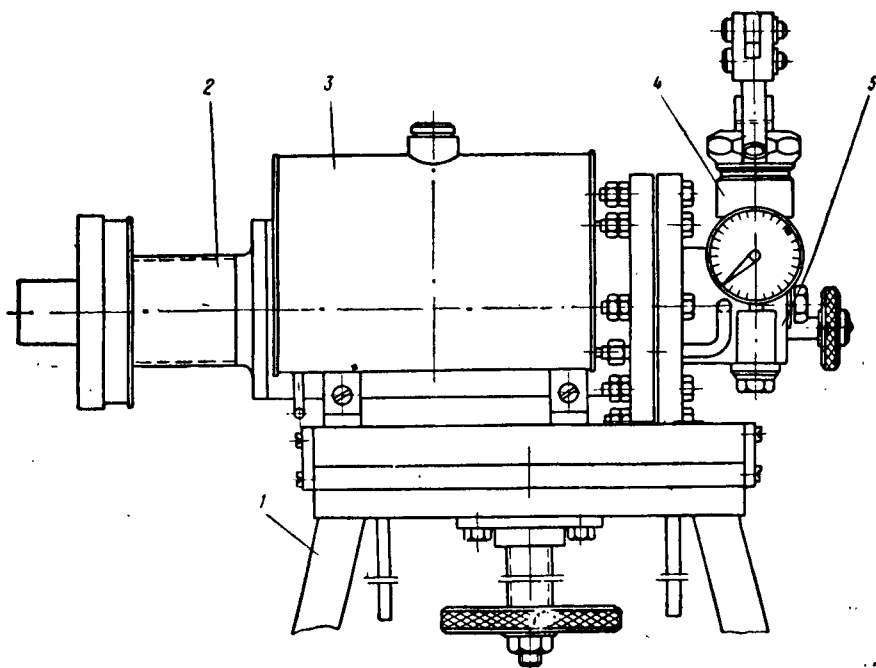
Гидравлический пресс для снятия роликовых подшипников, упорных и лабиринтовых втулок с вала якоря:
